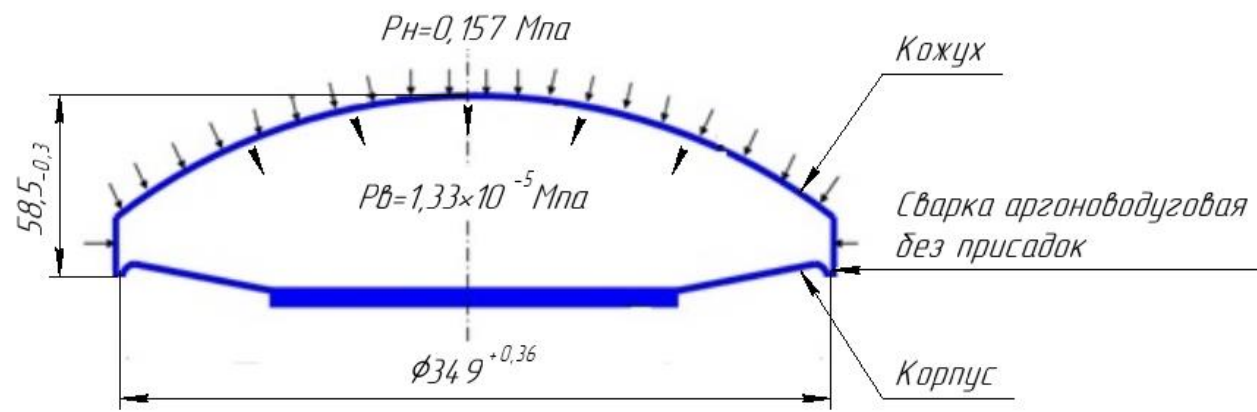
Эскиз детали «Кожух» в сборе с корпусом УДМ.
